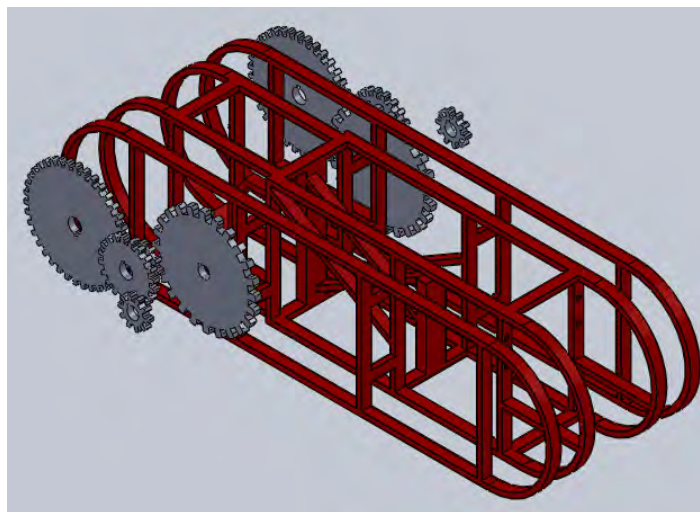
b) Se muestra una vista explosionada de los engranes.
